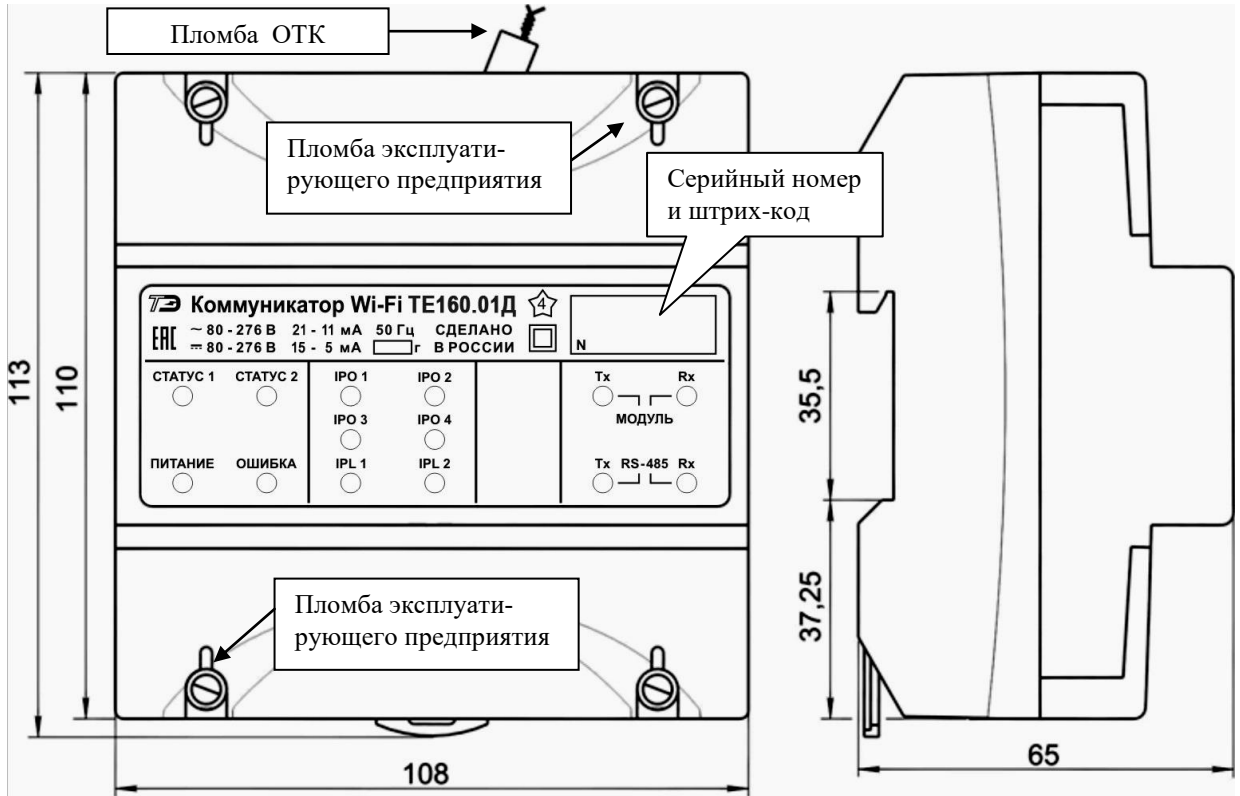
Габаритный чертеж и установочные размеры коммуникатора Wi-Fi TE160.01Д с защитными крышками
